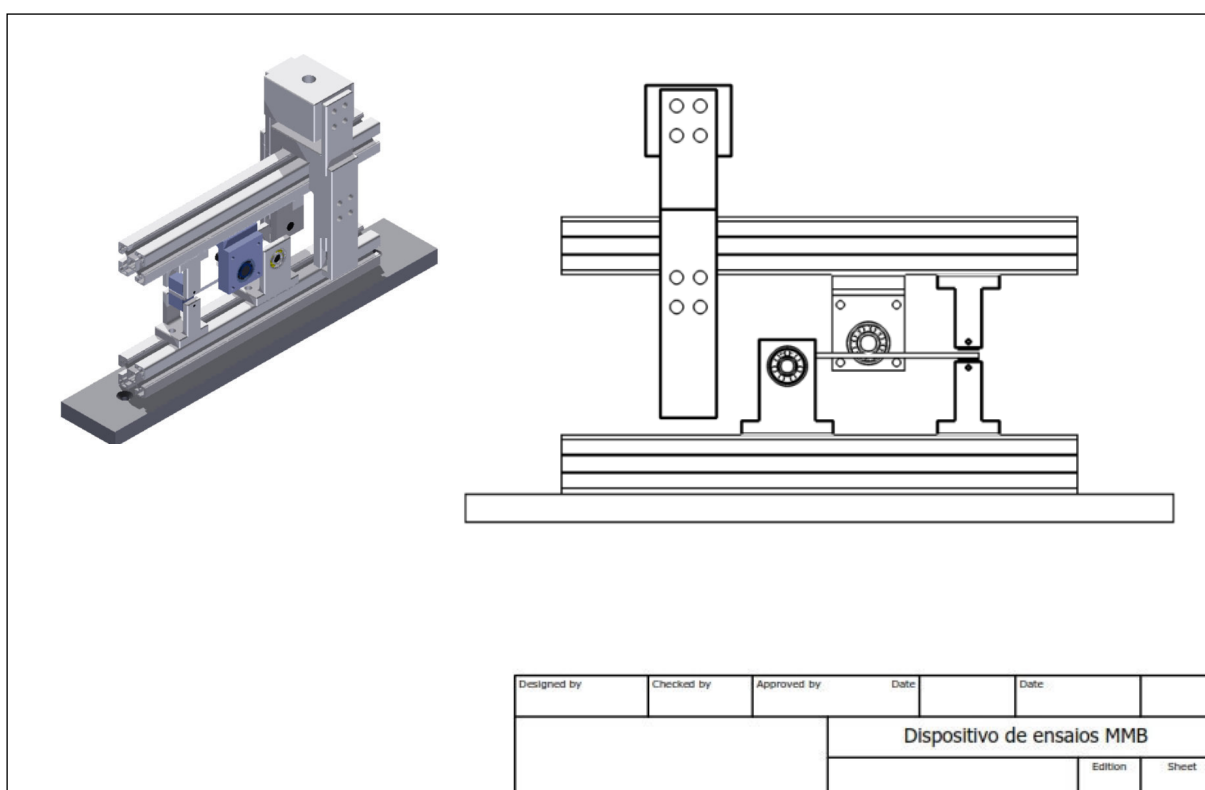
Desenho técnico de conjunto do dispositivo de ensaios MMB.
